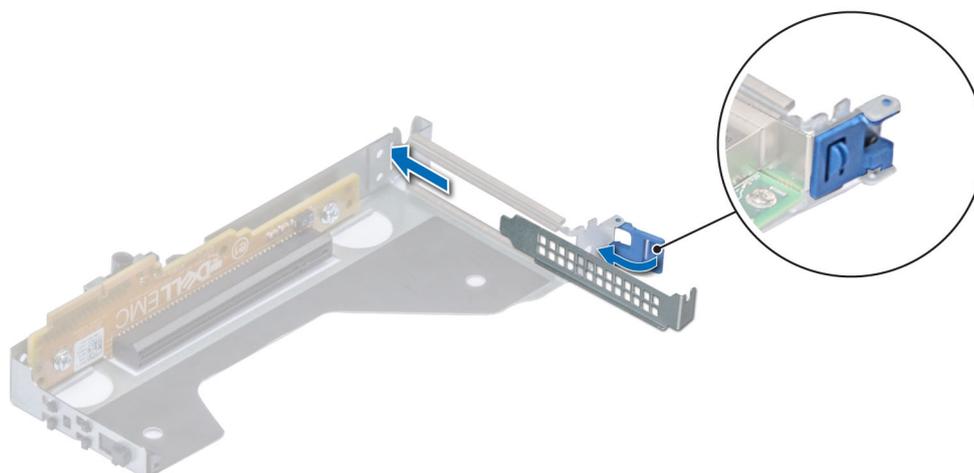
Installation de la plaque de recouvrement pour la carte de montage 2
